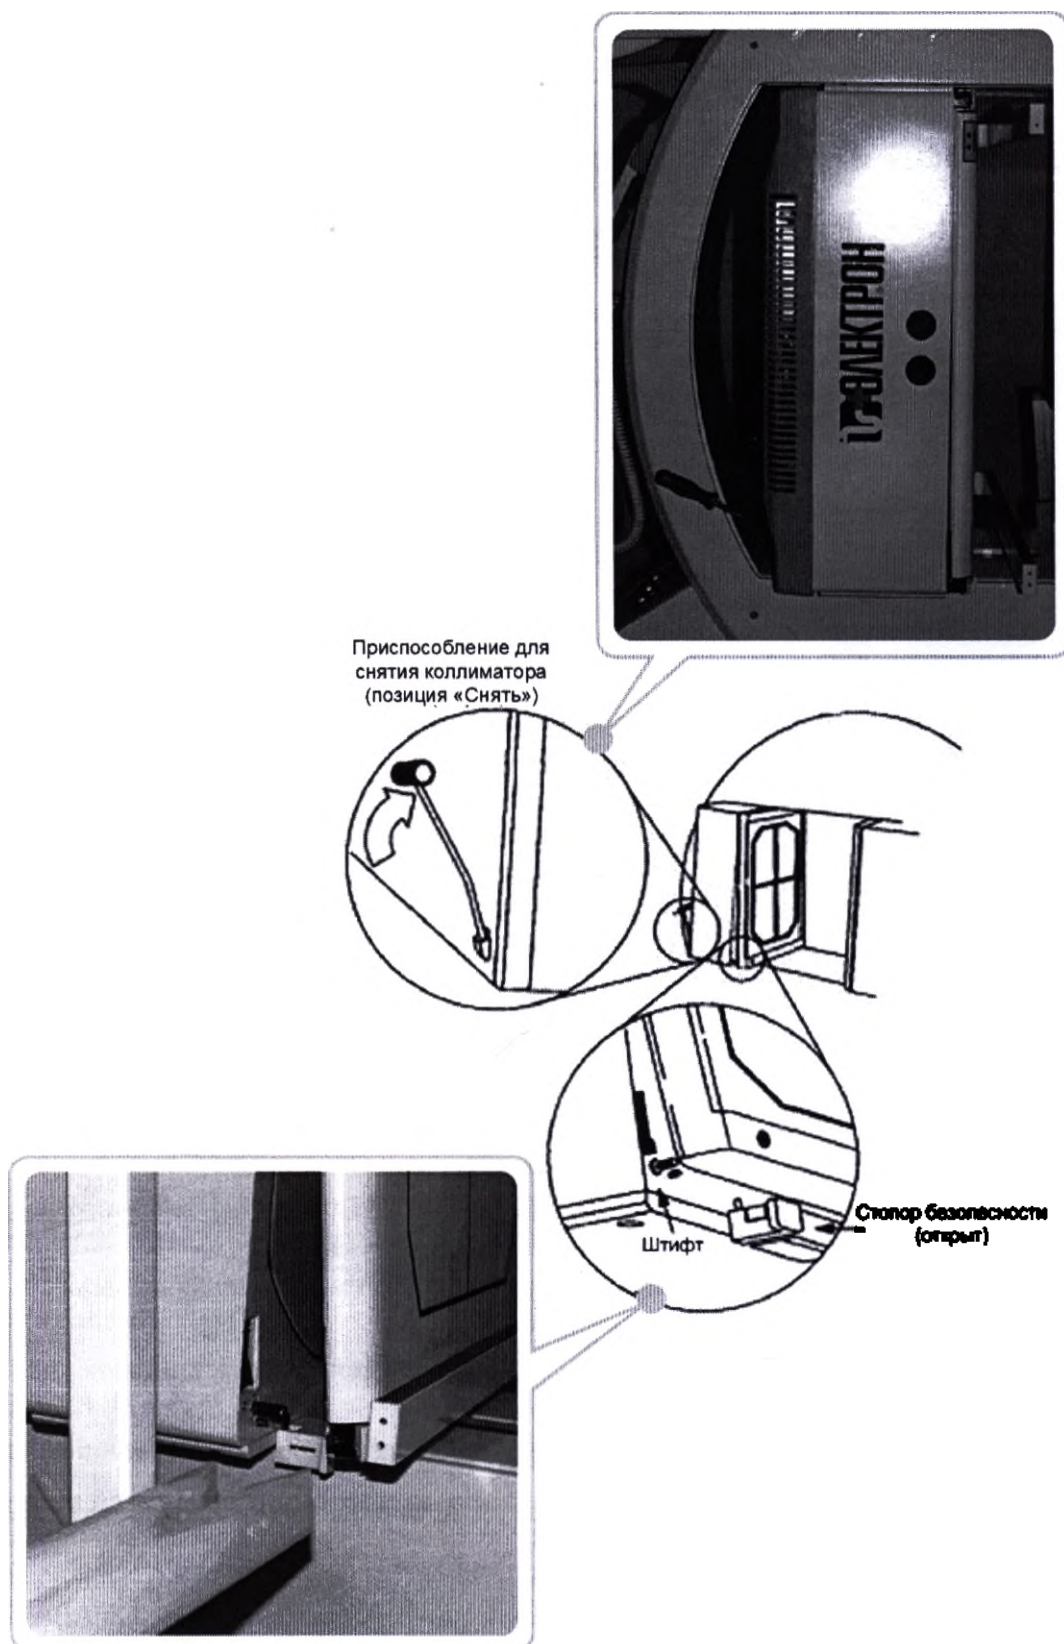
Приспособление и стопор в открытой позиции
